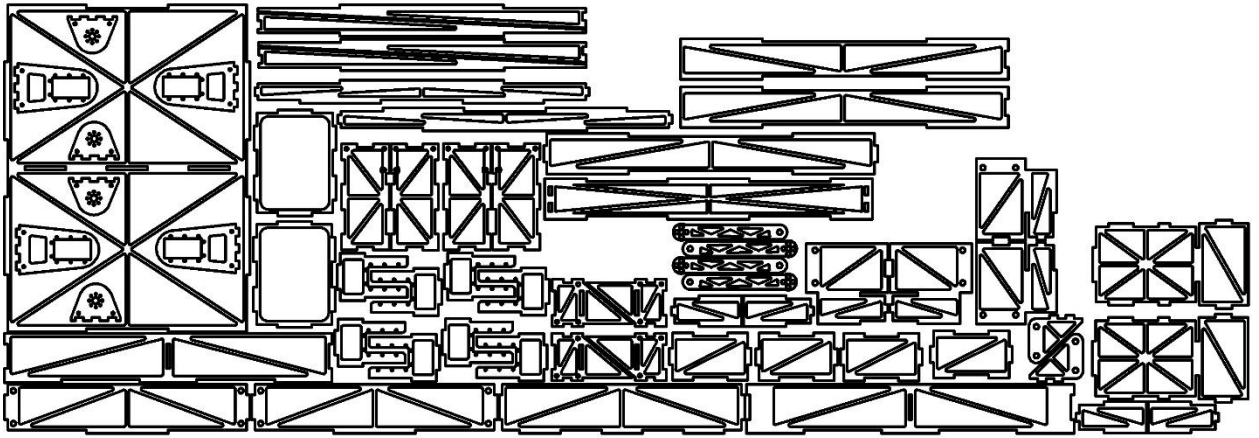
Макет розкладання деталей прототипу для лазерної різки
